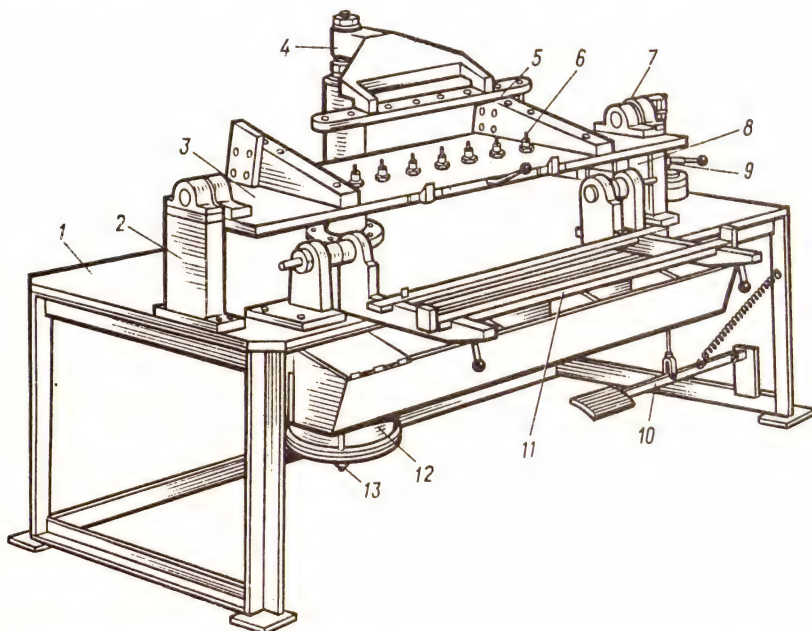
Стенд для разборки (сборки) головок блока цилиндров двигателей ЗИЛ-130:
